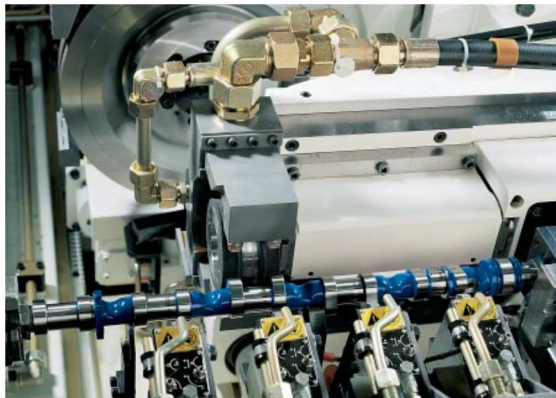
Шліфування кулачків розподільного вала на верстаті фірми Junker
